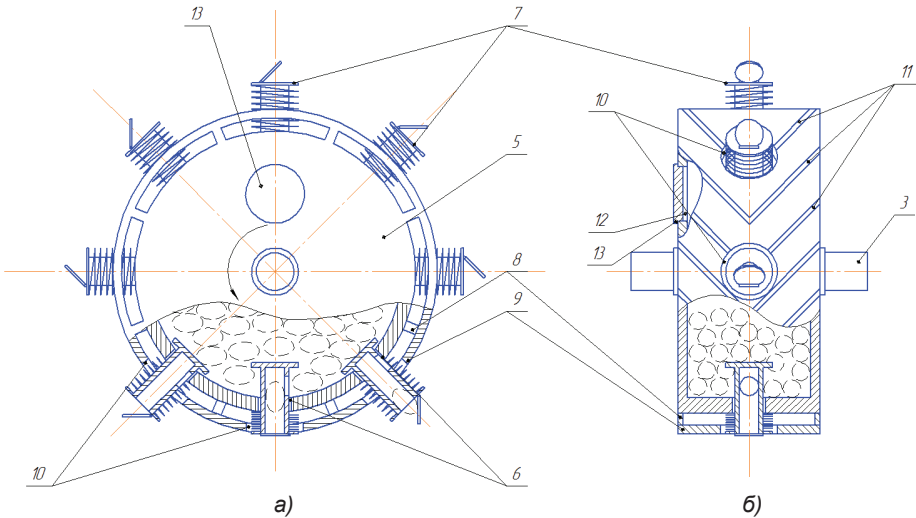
Высевающее устройство: а) главный вид, б) вид сбоку.
